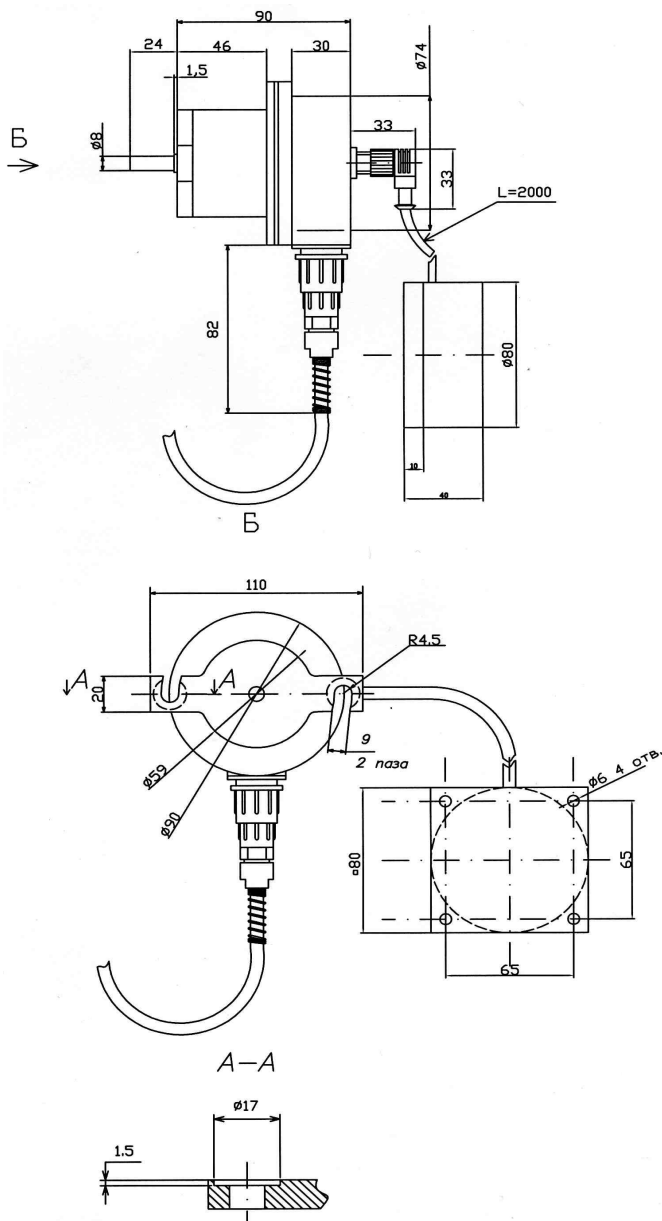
а- Габаритные и присоединительные размеры датчика пути с бесконтактным выключателем.
